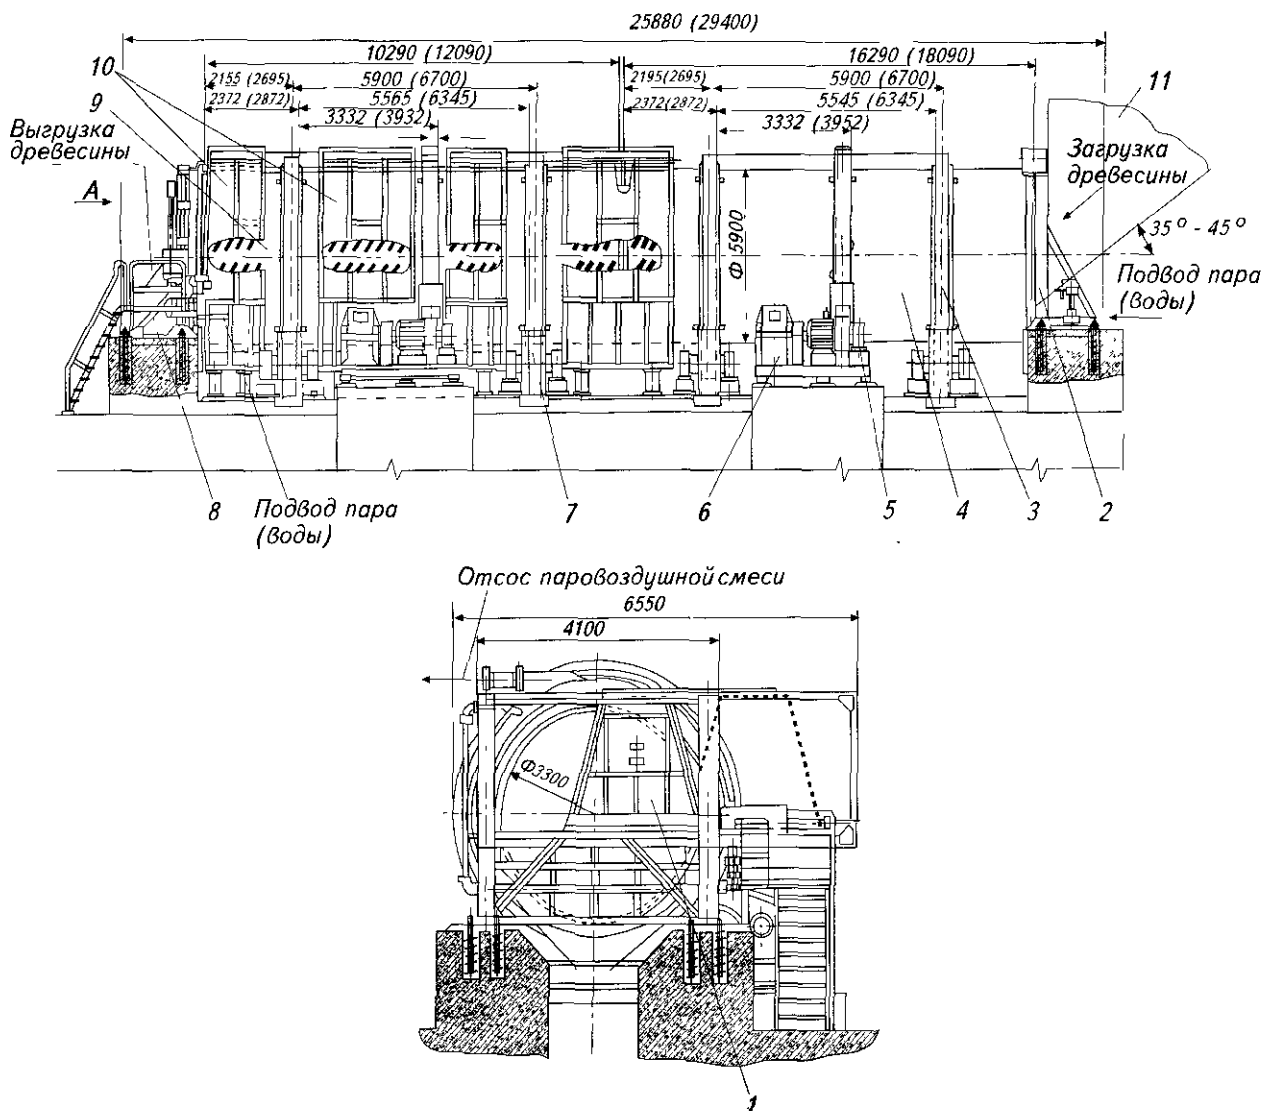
Корообдирочный барабан КБ-420А (КБ-425А):
